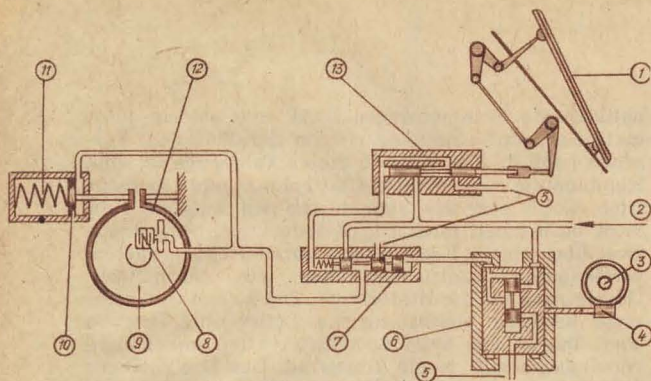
Selbsttätige Steuerung des Getriebes nach Abb. 5
